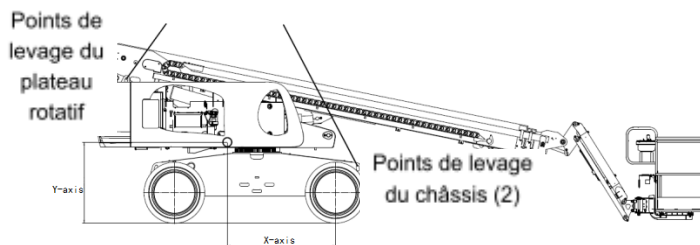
Schéma de principe pour fixer la machine pendant le levage
